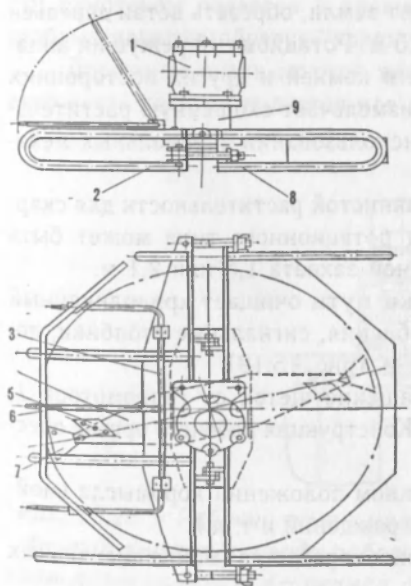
Режущий аппарат ротационной косилки: 1 – гидромотор привода режущего аппарата; 2, 8 – секции защитного ограждения; 3 – поворотная решетка; 4 – ротор; 5, 7 – ножи; 6 – отражатель; 9 – корпус.
